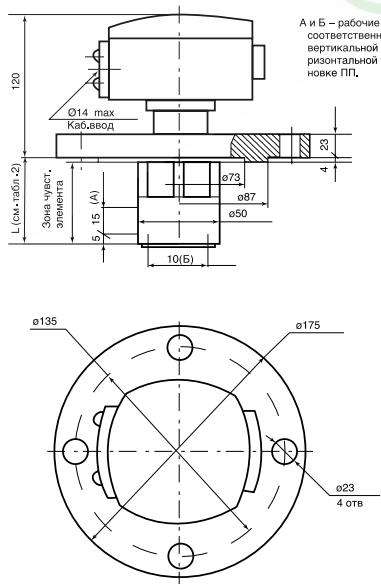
Габаритные и установочные размеры преобразователей первичных ПП-071 для РОС-101 и ПП-171 для РОС-102
